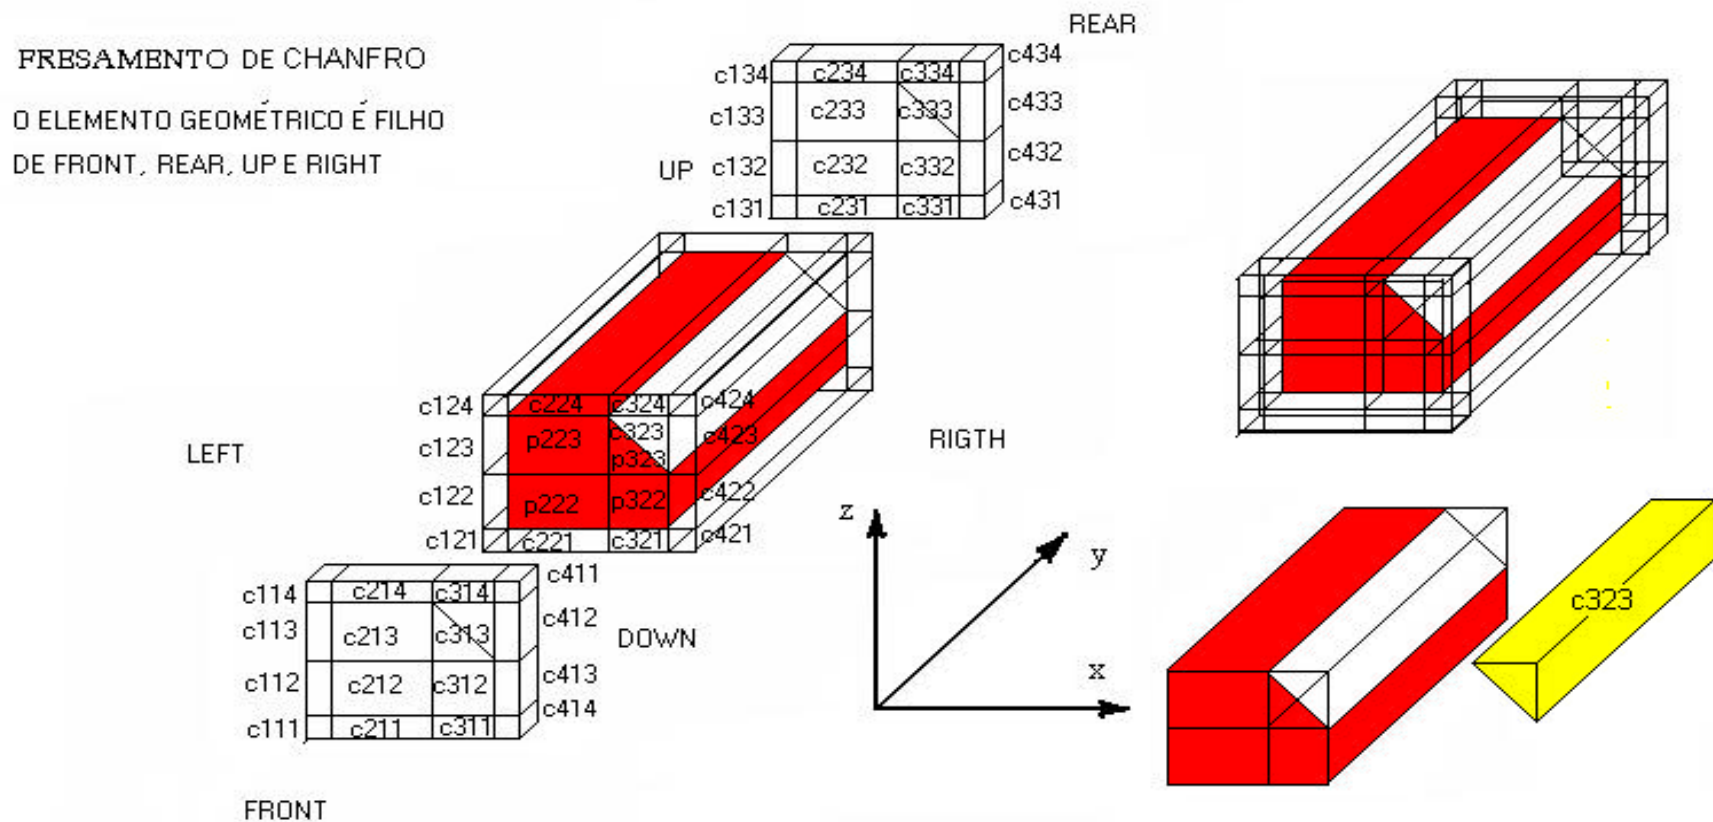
Usinagem de chanfros “set-up’s” e fases de usinagem
